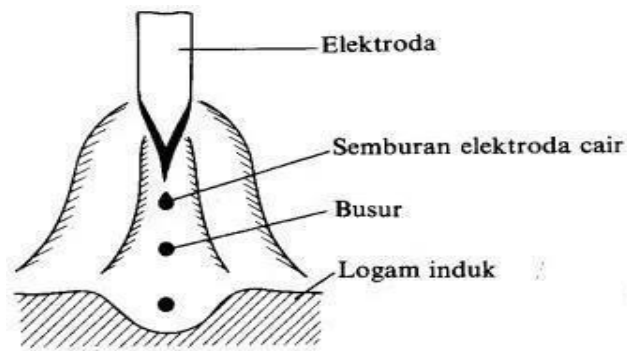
Ilustrasi *Gas Metal Arc Welding* (GMAW).
